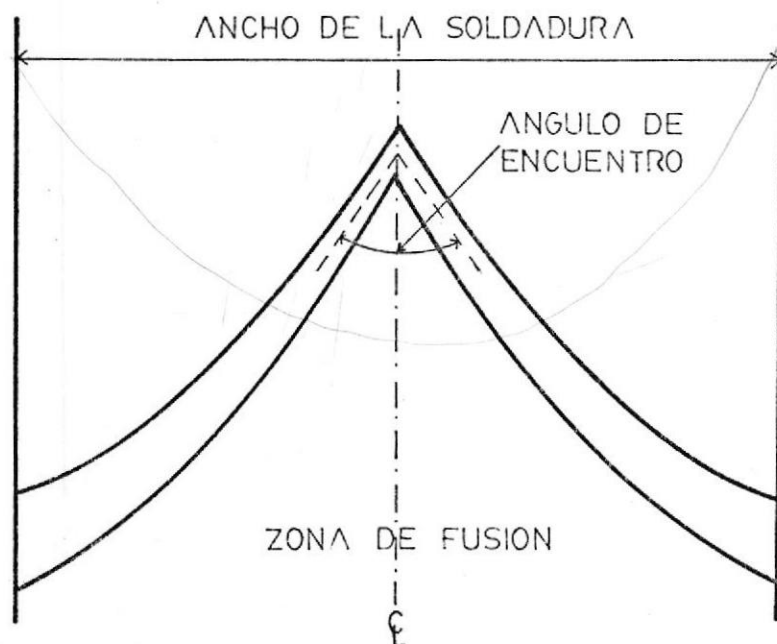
Representación esquemática de una sección vertical de la soldadura mostrando el ángulo de encuentro (Ref. 3).
